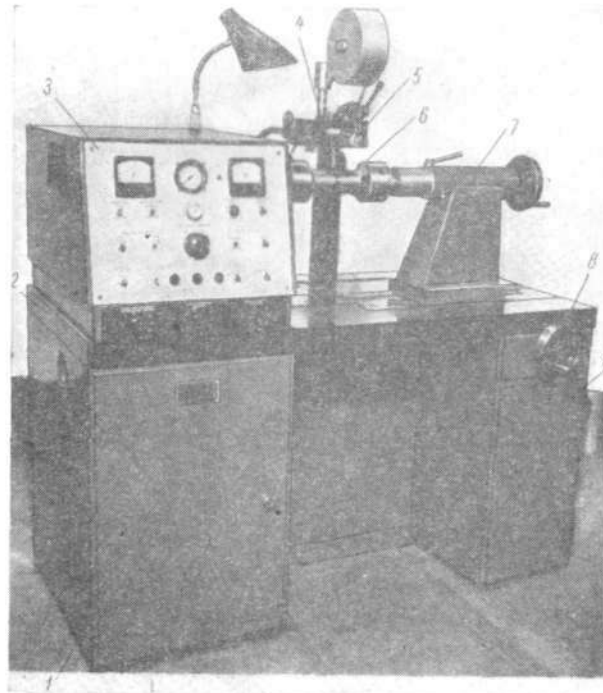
Автомат «Маяк» для сварки кольцевых стыков на цилиндрических изделиях.
